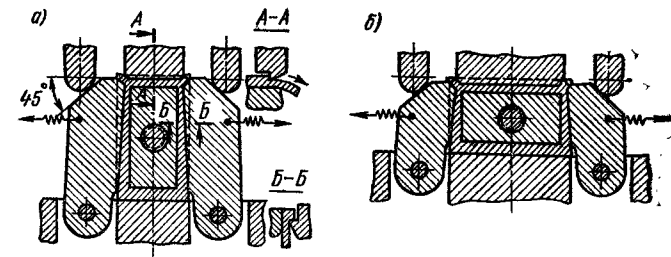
Схема действия штампа для гибки прямоугольных труб
